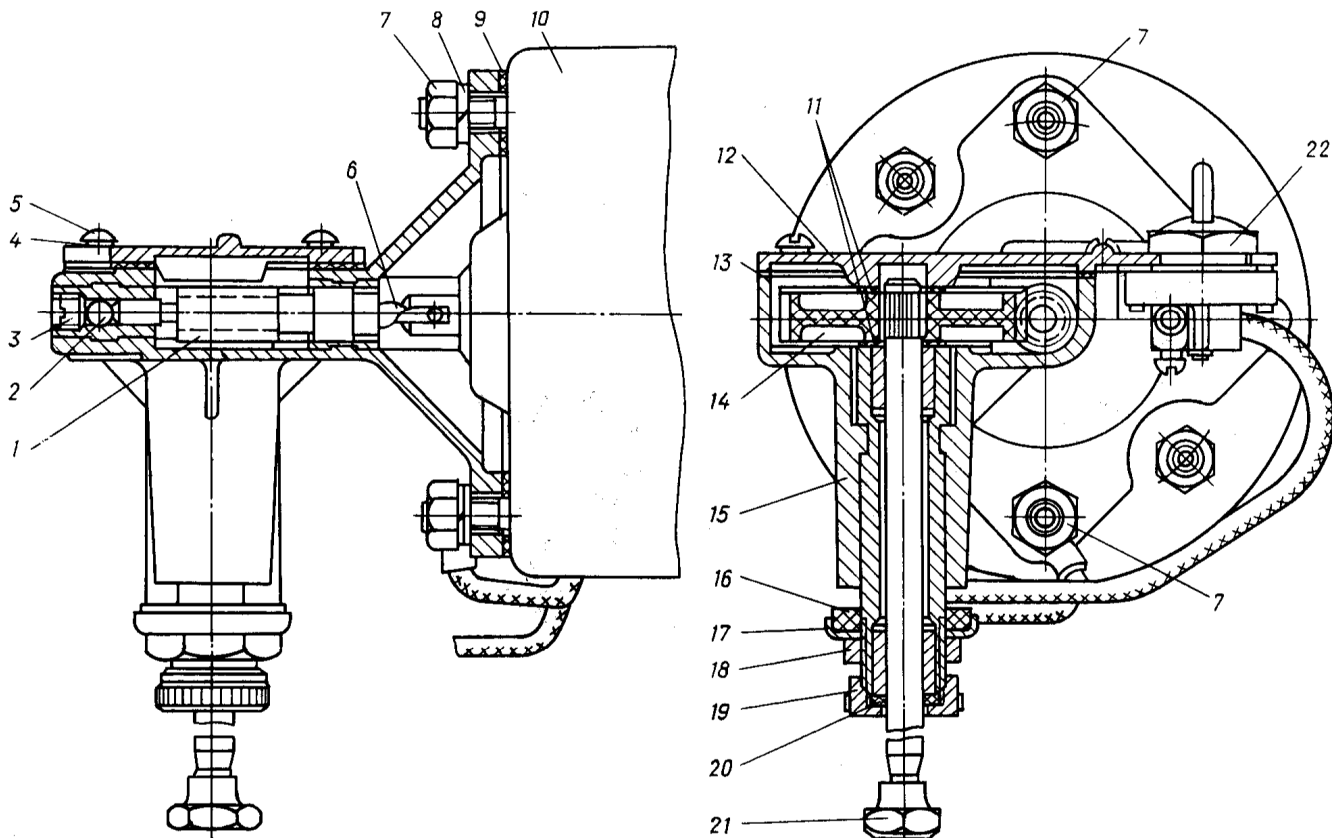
Редуктор стеклоочистителя с электродвигателем в сборе:
